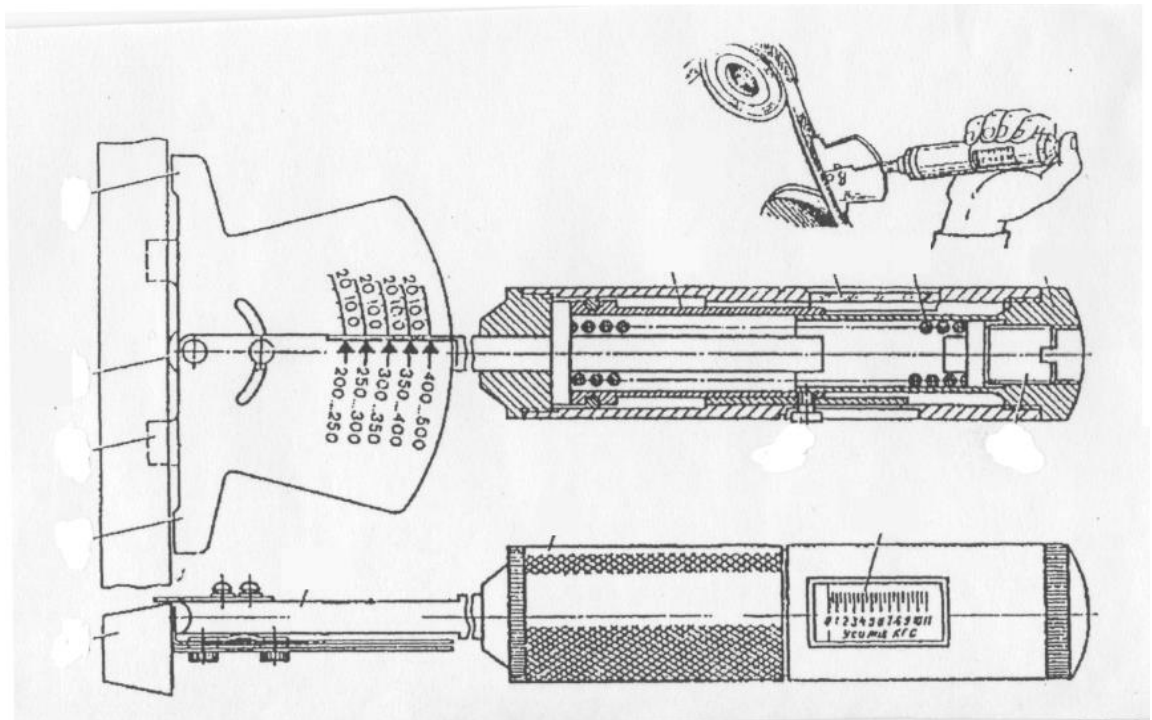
Прибор для проверки натяжения ремней КИ-8920.
